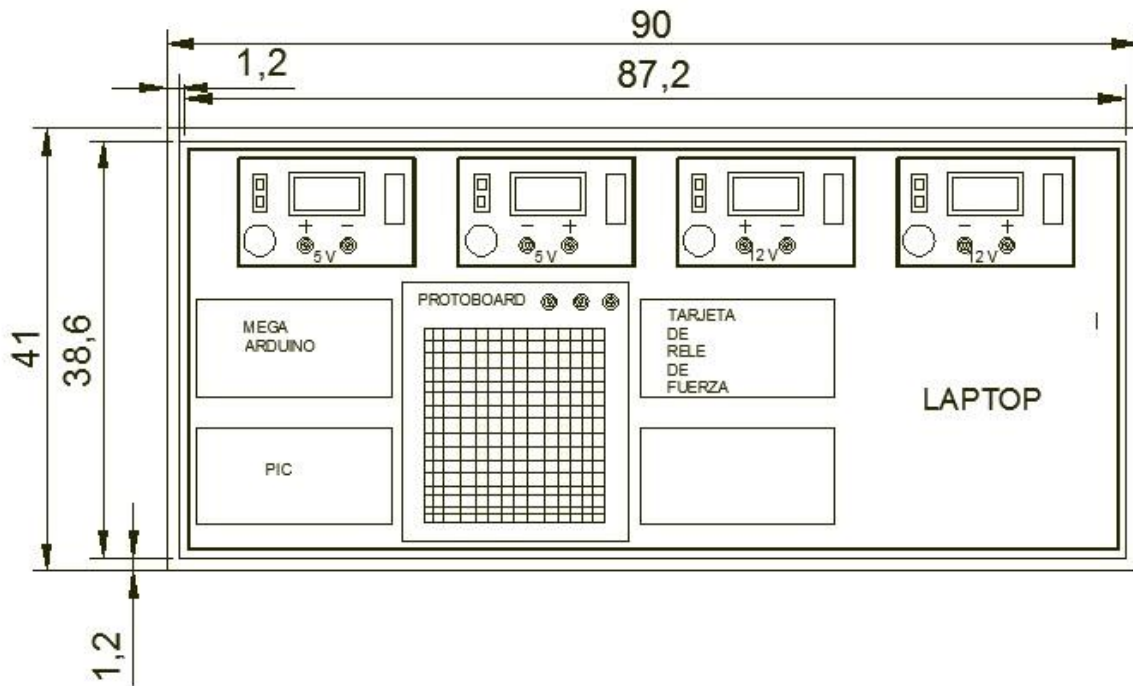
3: DISEÑO ESQUEMÁTICO PARTE BAJA EN CAD DEL MÓDULO.
